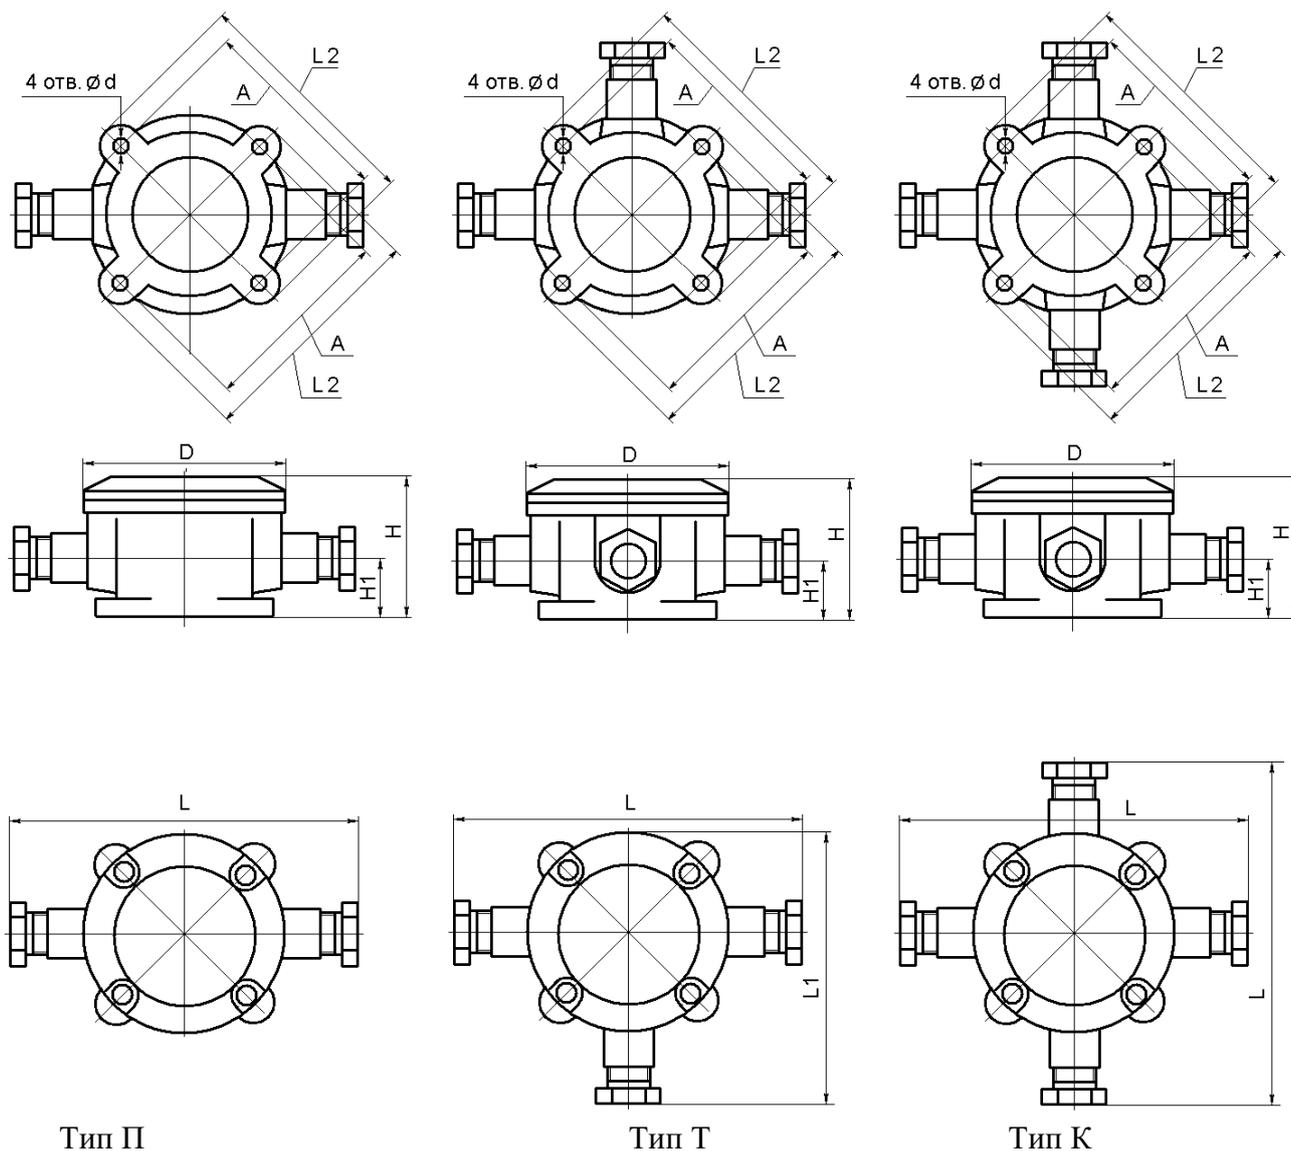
Габаритные, установочные и присоединительные размеры коробок ЕхКСУВ-А без вводного устройства в дне коробки. Остальное – см. рисунок А.3
